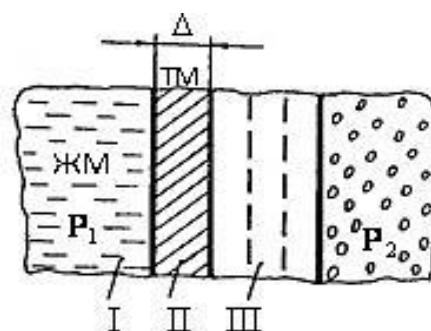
Схема расположения областей системы: I – жидкий металл; II – затвердевший металл; III – форма; P_1 и P_2 – силы давления на оболочковую форму со стороны металла и опорного наполнителя
